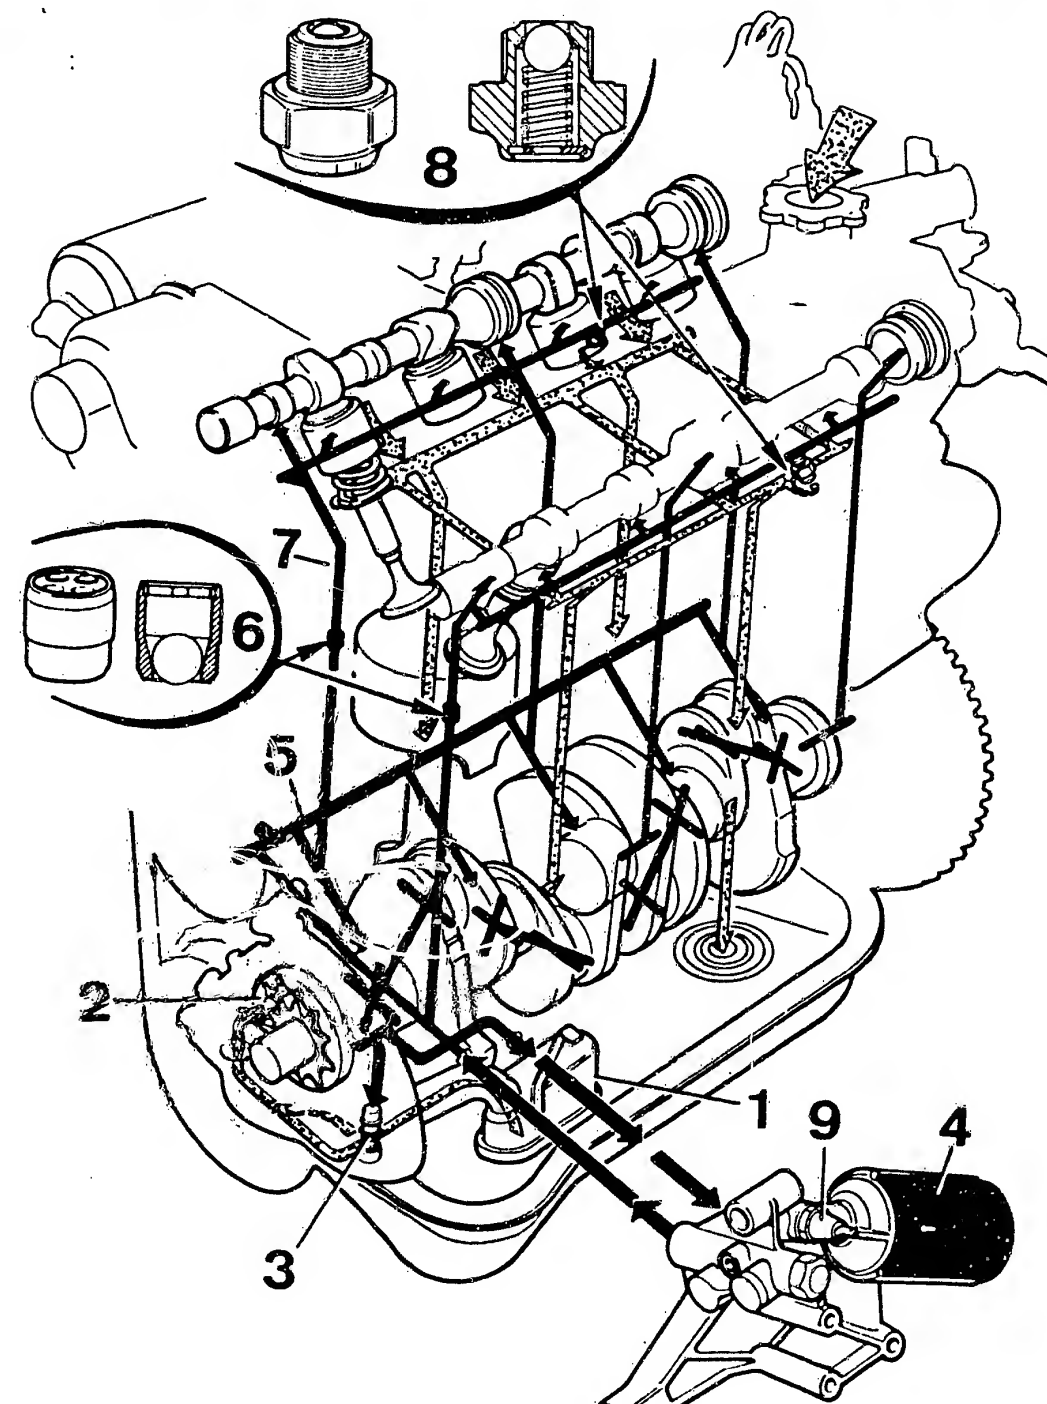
Motor 2000 i.e. mit hydraulischen Ventilstößeln: 1 Ansaugsieb – 2 Ölpumpe – 3 Überdruckventil – 4 Ölfilter – 5 Druckleitung – 6 Rückschlagventil – 7 Steigleitung – 8 Druckbegrenzer für die hydraulischen Stößel – 9 Öldruckschalter.
